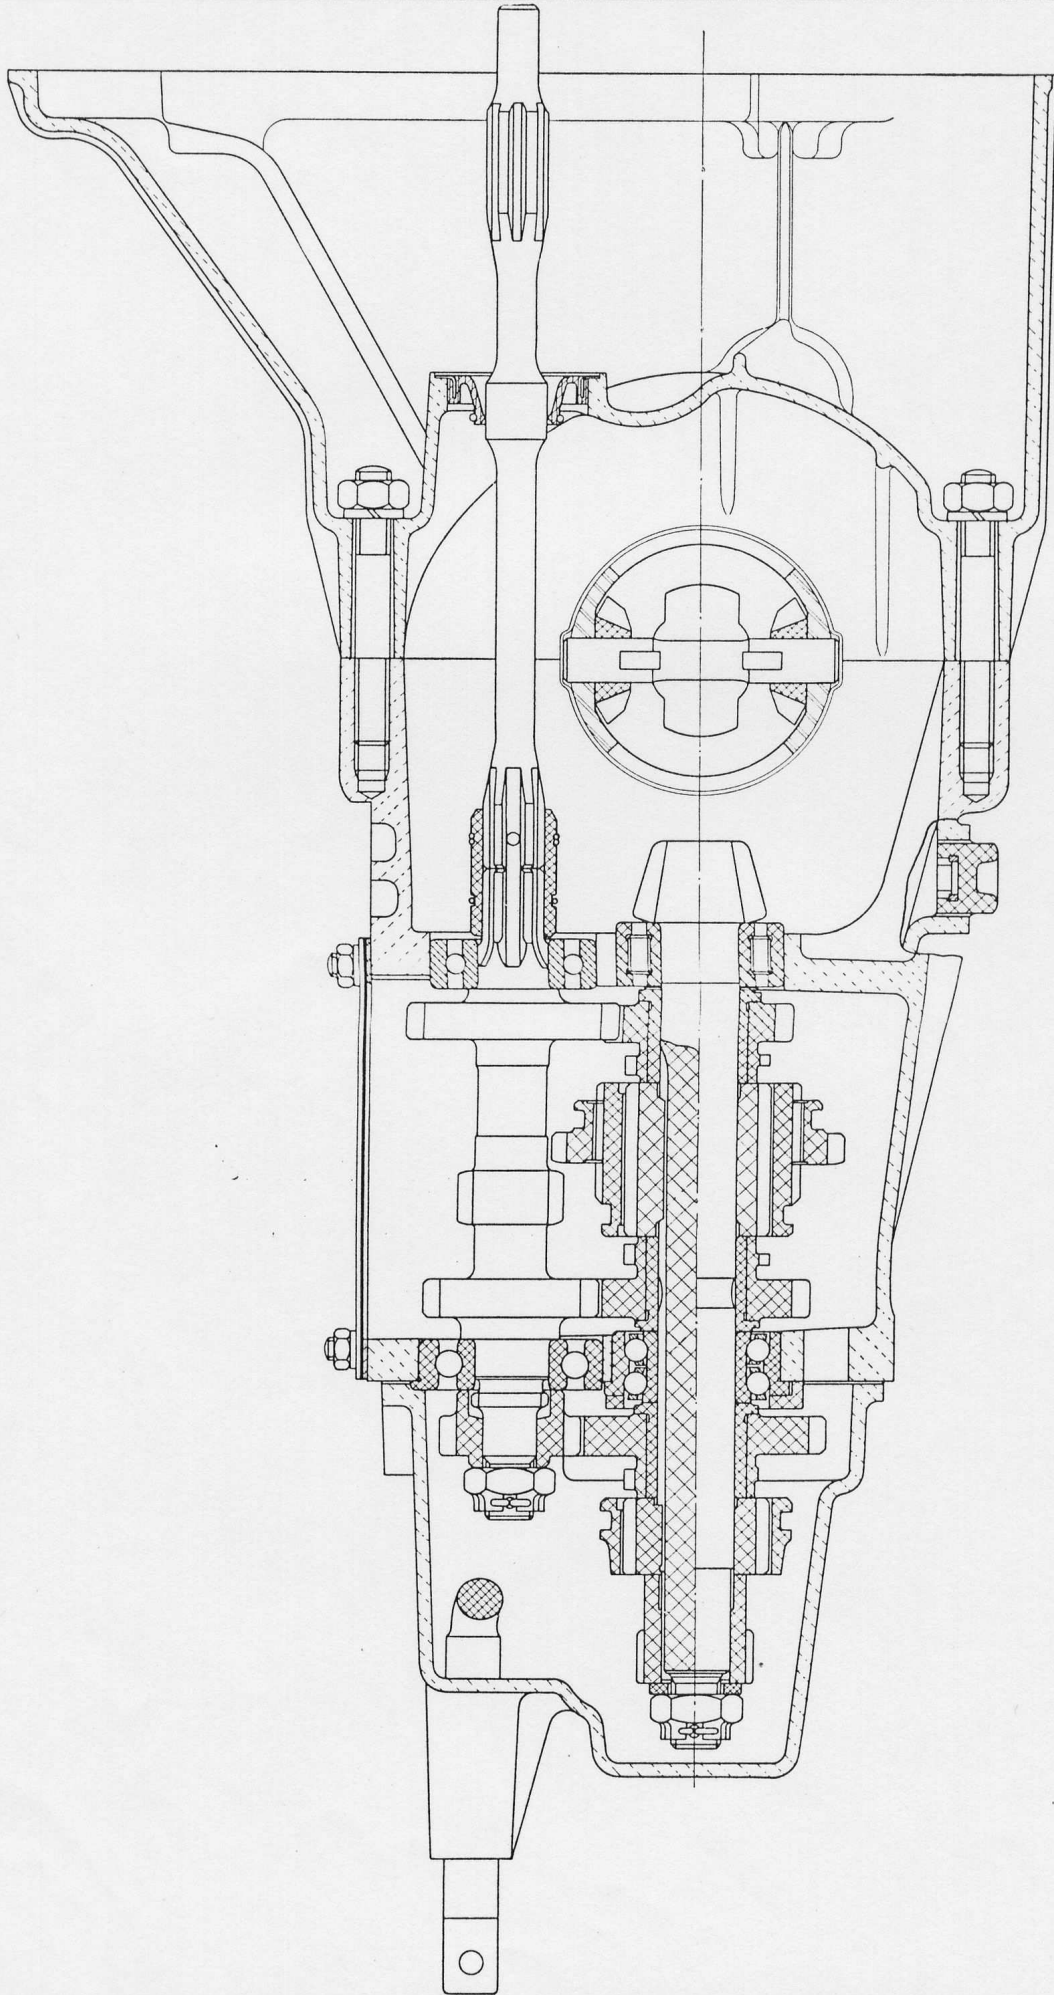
Längsschnitt des Wechsel- und Ausgleichgetriebes.
